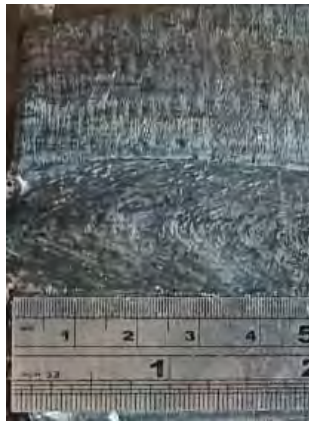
Aspecto exterior del cordón de soldadura - Prueba 1
